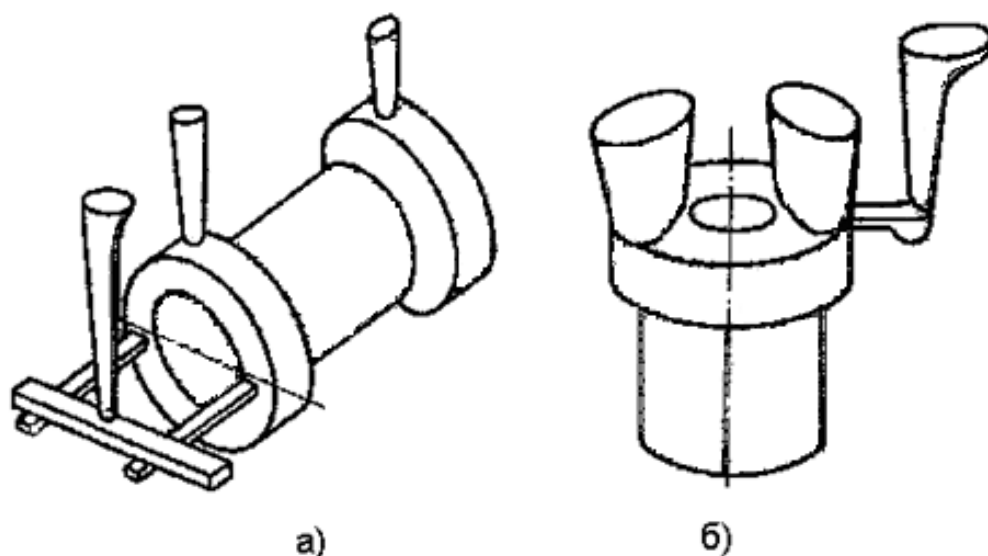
Эскизы готовых отливок с литниковой системой:
